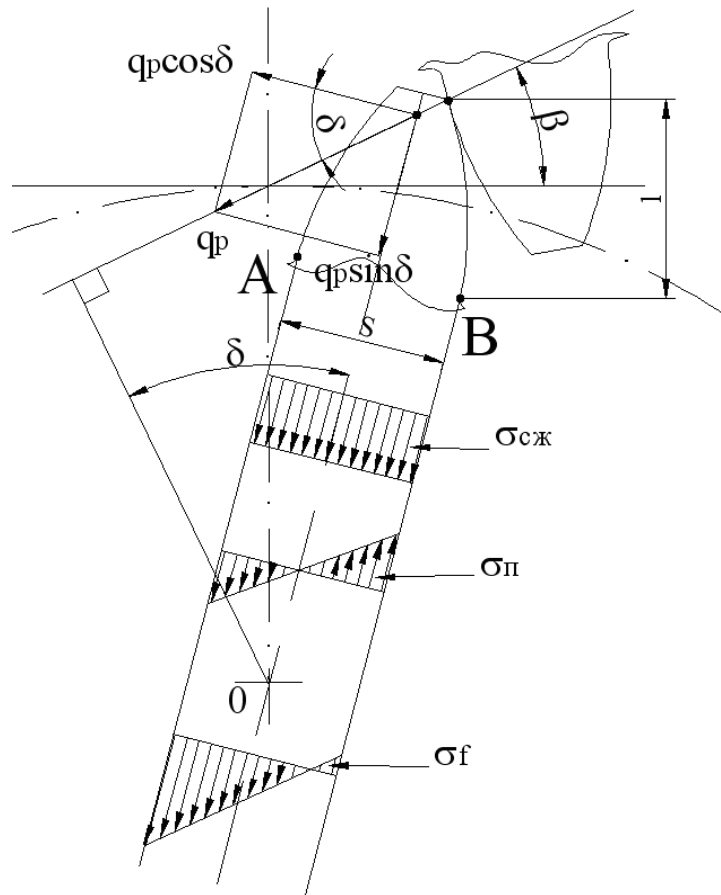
Схема сил та напружень, що діють на зуб циліндричного прямозубого колеса.
